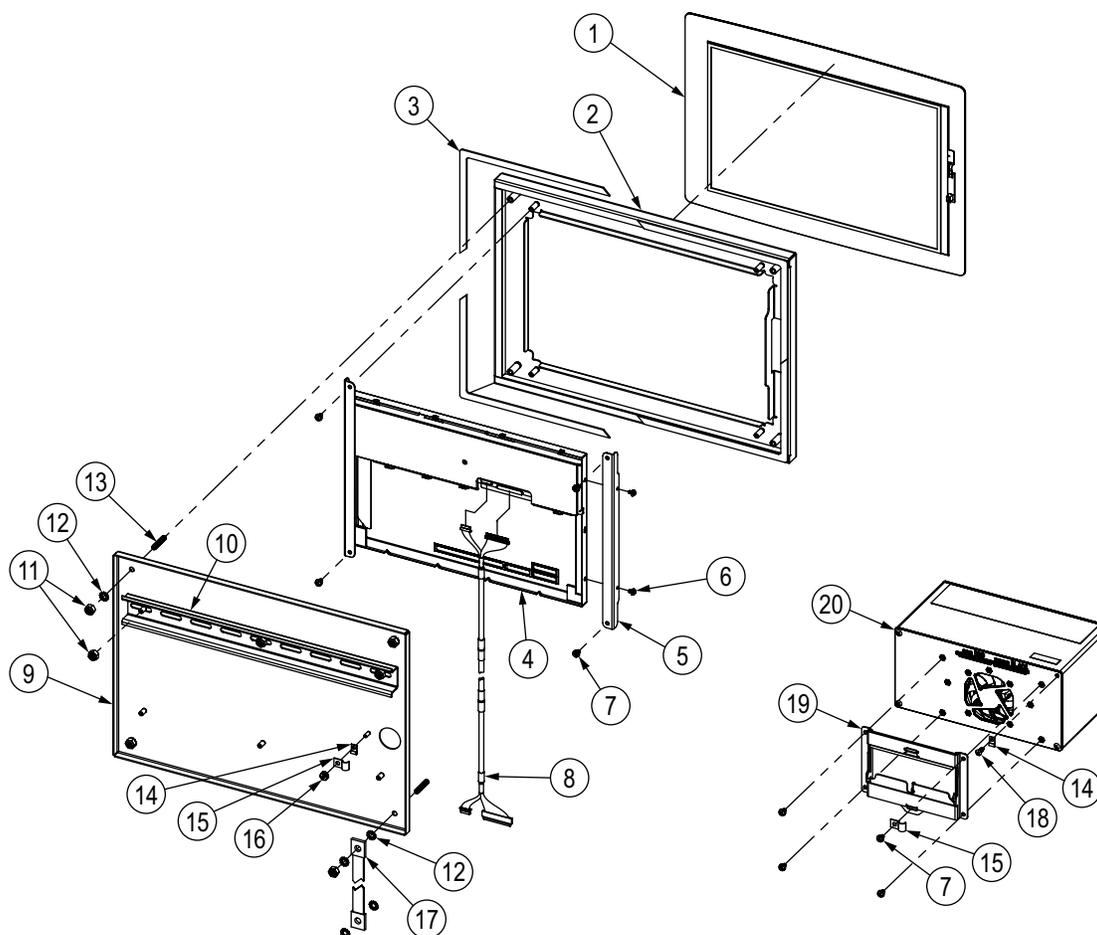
Componenti per la riparazione dell'indicatore da 12" con montaggio a pannello solo touch
